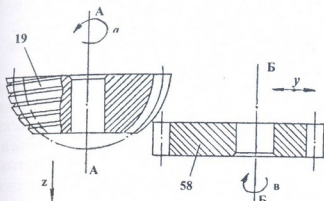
Схема нарезания некруглого цилиндрического колеса наружными зубьями
